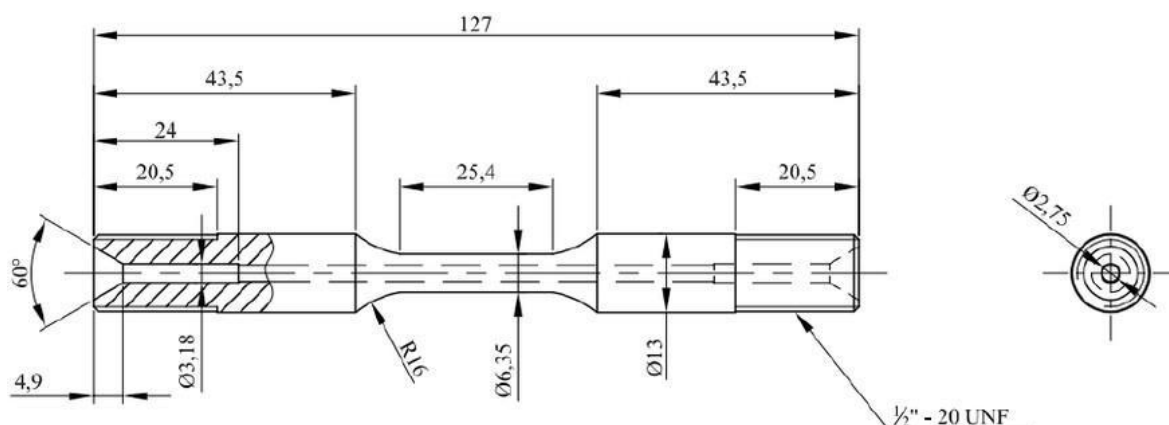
Desenho técnico do corpo de prova utilizado no ensaio por BTM modificado.
